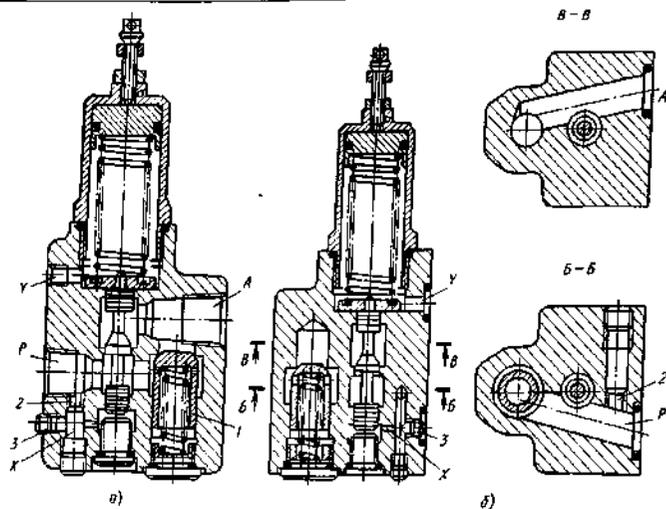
Конструкция гидроклапанов давления с обратным клапаном типа Г66-3 резьбового (а) и стикового (б) присоединенный
